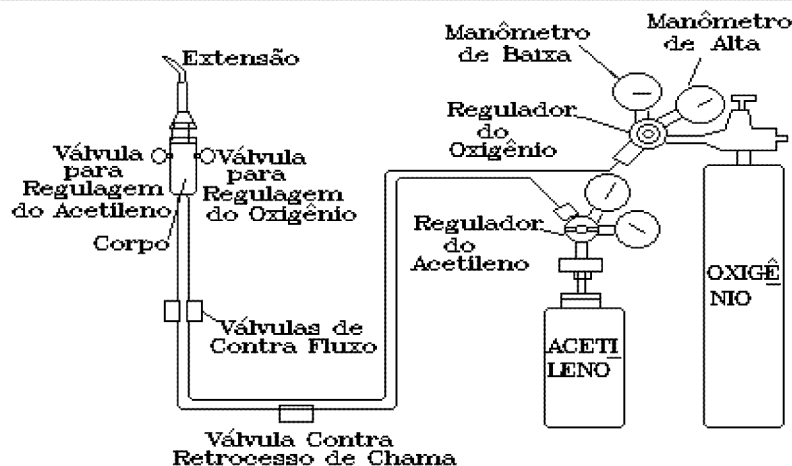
Equipamento Básico para a Soldagem com Oxi-Acetileno.
